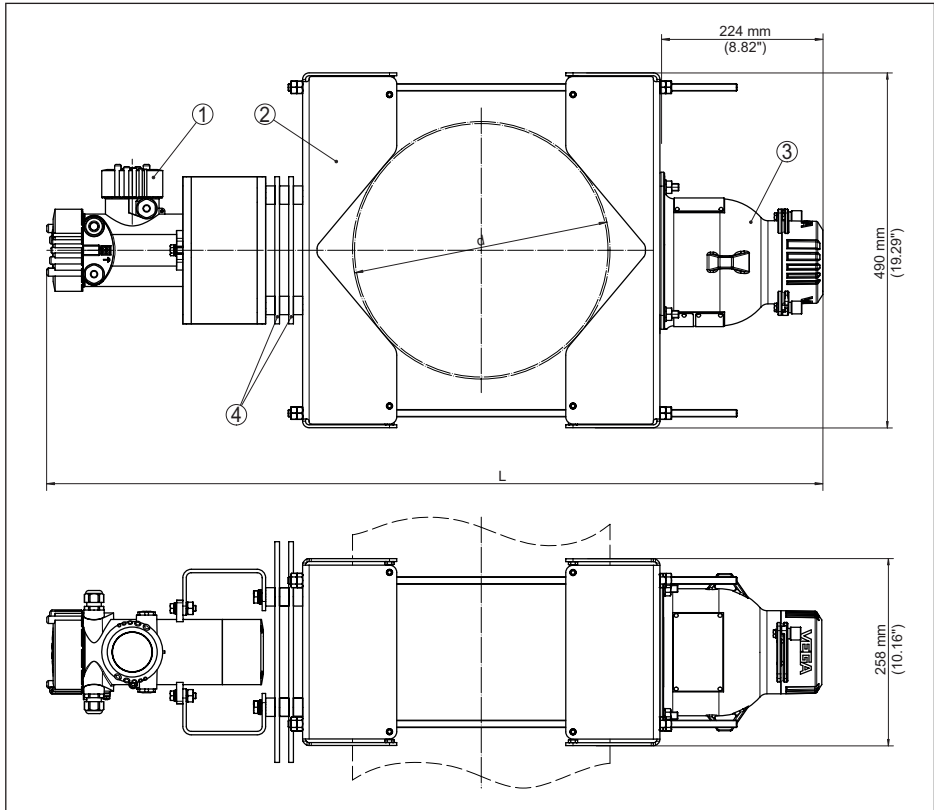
Dispositivo de sujeción con sensor montado horizontalmente y kit de protección térmica (con VEGA-SOURCE 81, 82, 83)
